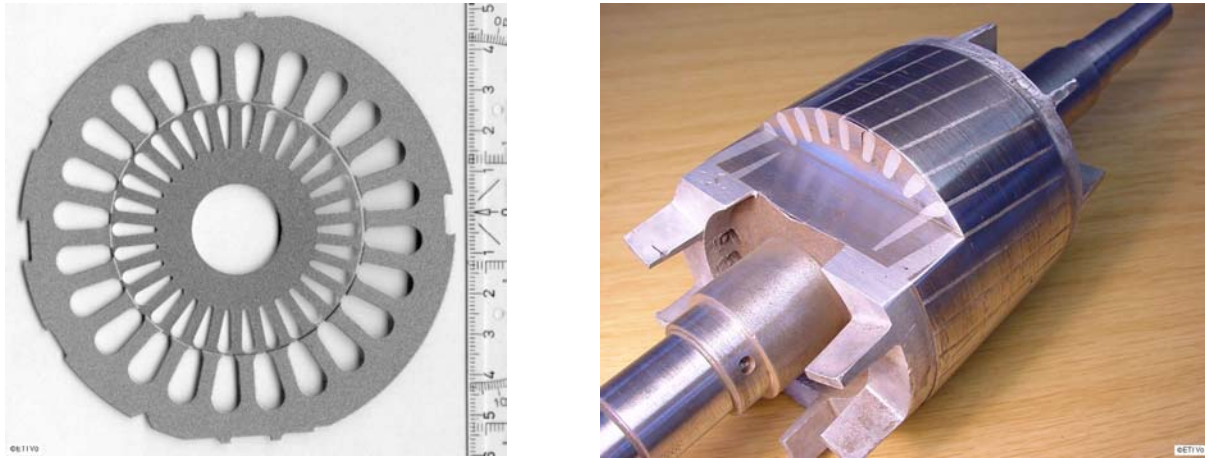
Blechschnitt einer vierpoligen (2 Polpaare $p=2$) Asynchronmaschine mit 24 Ständernuten Leistung 550 W $n=1470$ 1/min. Das Rotorblech paßt erst nach dem Abdrehen in die Bohrung des Ständers (links). Aufgeschnittener Rotor mit eingegossenen Aluminiumstäben.
